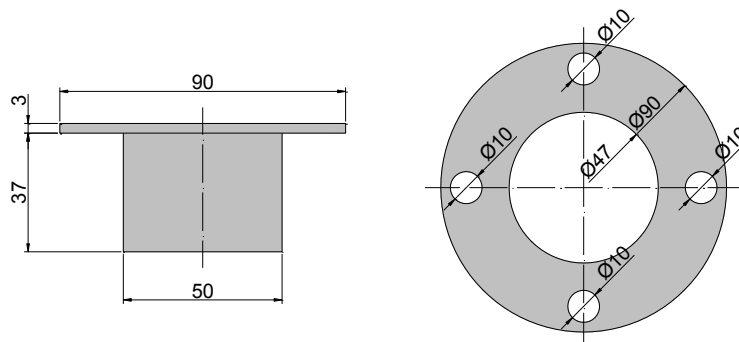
Corpo da Autoclave, em perfil e planta, respetivamente
